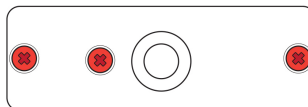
Befestigungsstellen an der Rückseite des Gehäuses
